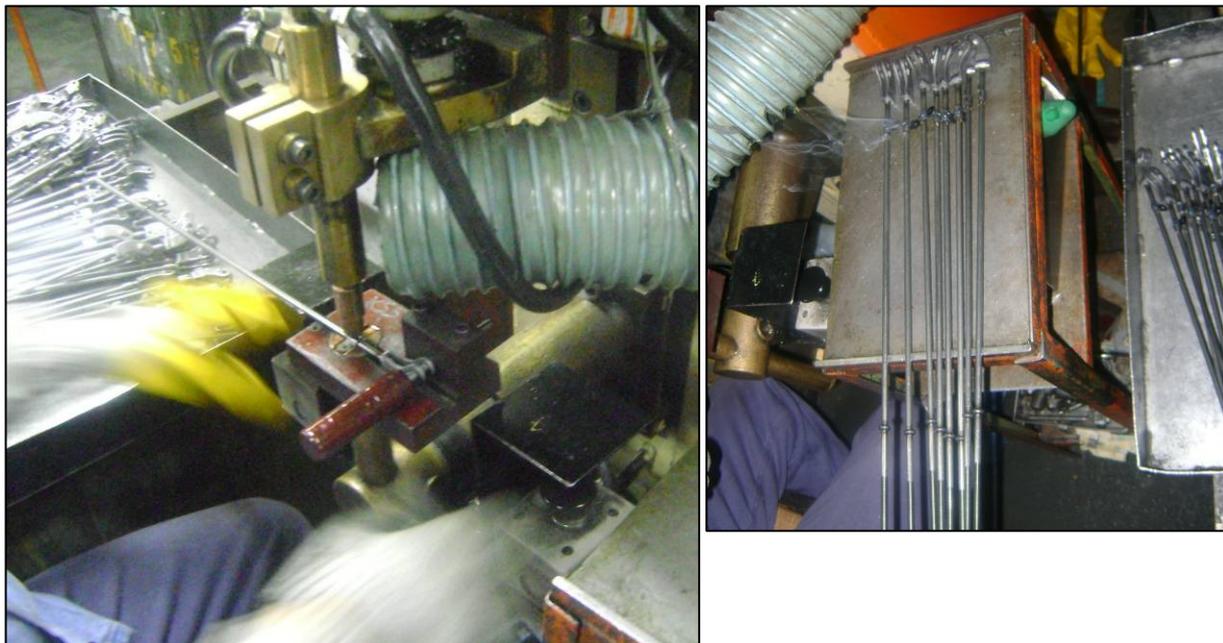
Oitavo processo, solda por resistência (solda ponto) do “Stopper”: À esquerda detalhe do dispositivo e equipamento. À direita varetas com “Stopper” soldado.
